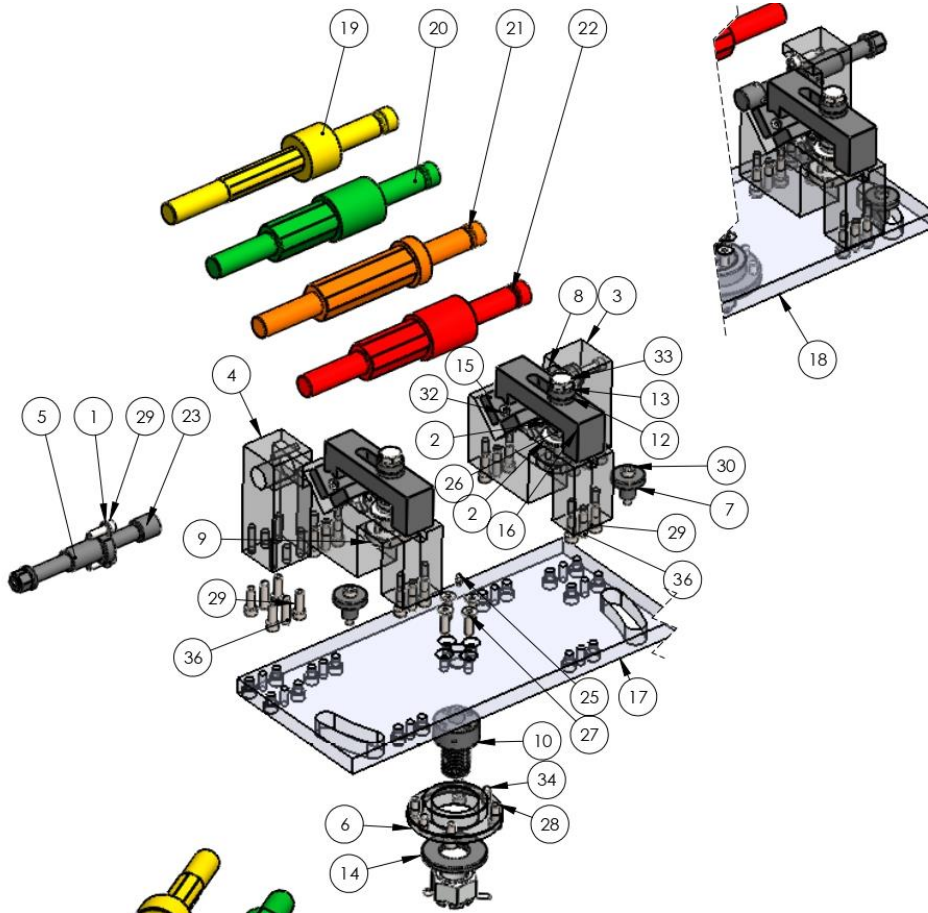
Projeto final chapa base + montagem final do sistema de giro
